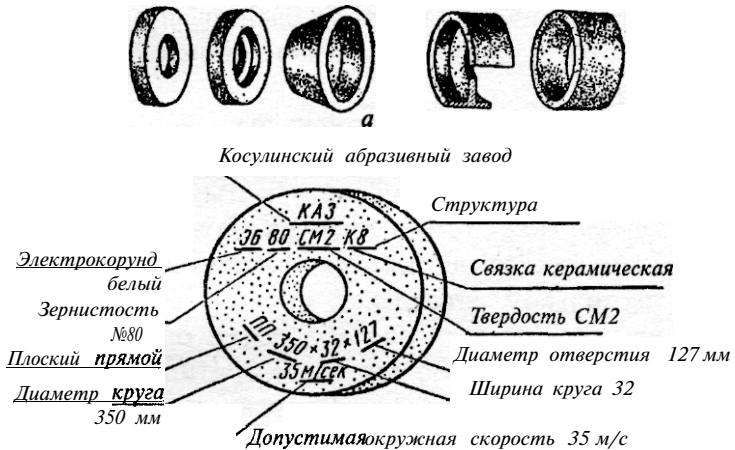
Формы шлифовальных кругов (а), маркировка круга (б)
